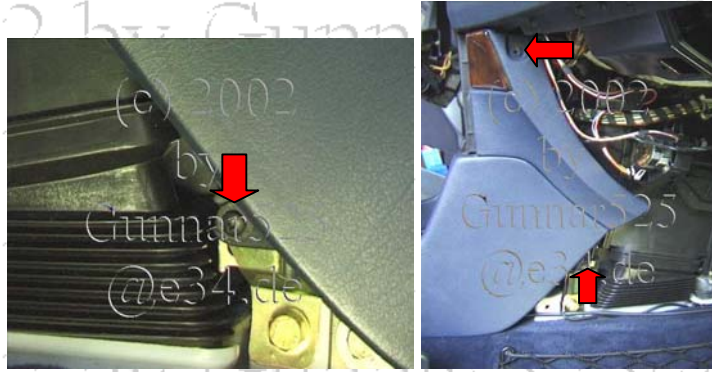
Schrauben (links und rechts) der Mittelkonsole
